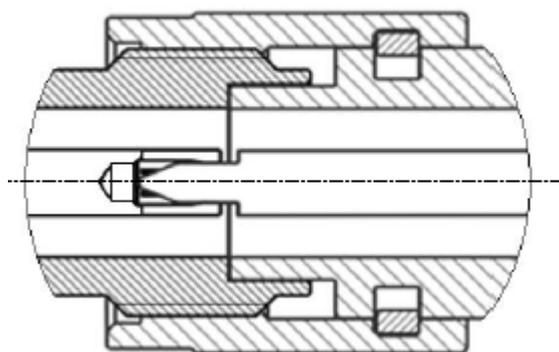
Соединители тип 3,5 мм (розетка слева, вилка справа)
